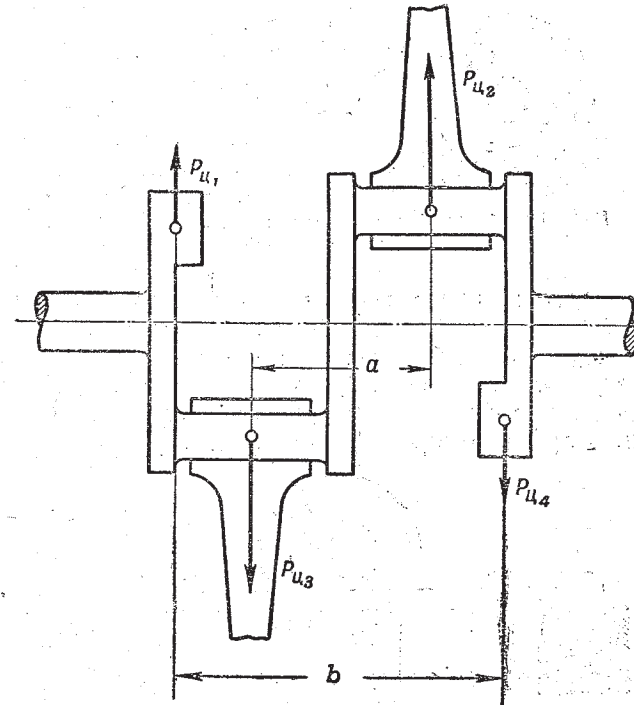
Силы инерции в кривошипном механизме двухцилиндрового двигателя:
